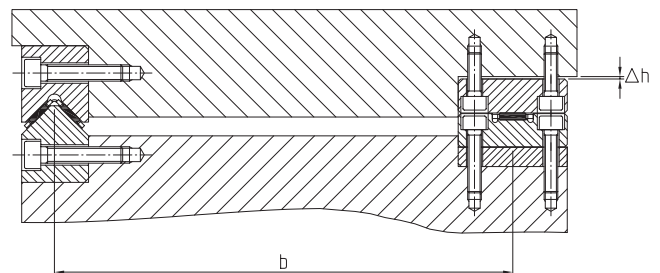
Compensation de la différence de hauteur à l'aide d'une cale dans le cas d'une construction ouverte.
